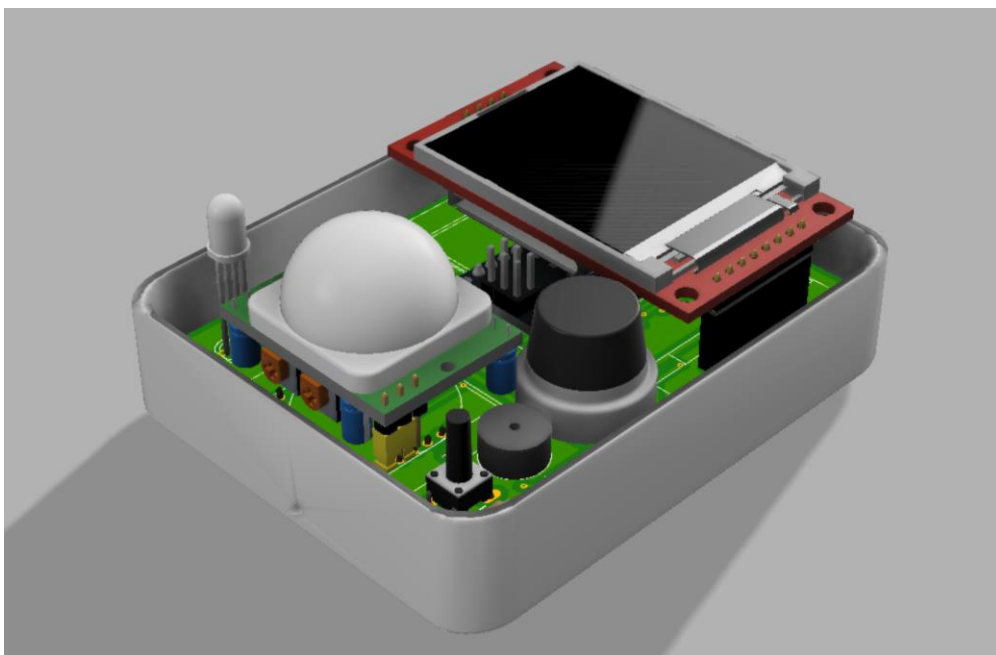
Rendering 3D del PCB , realizzati su Fusion 360
